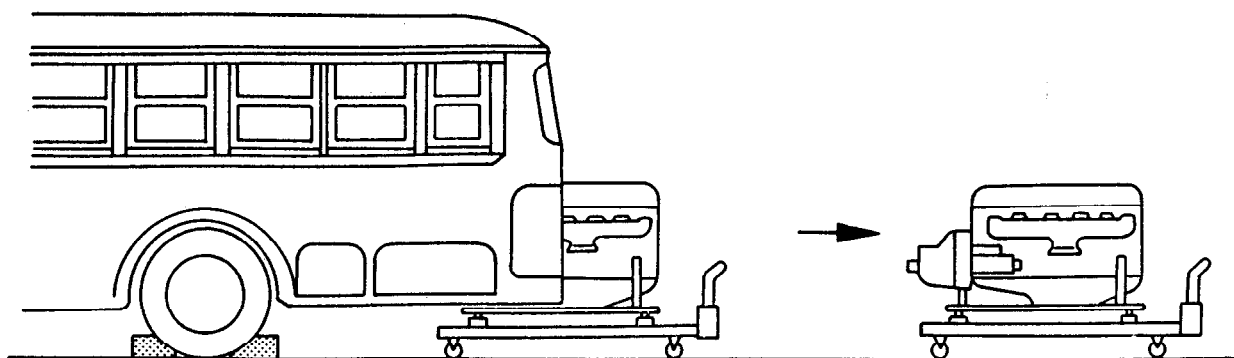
Desmontaje del motor en la parte posterior de un autobús
